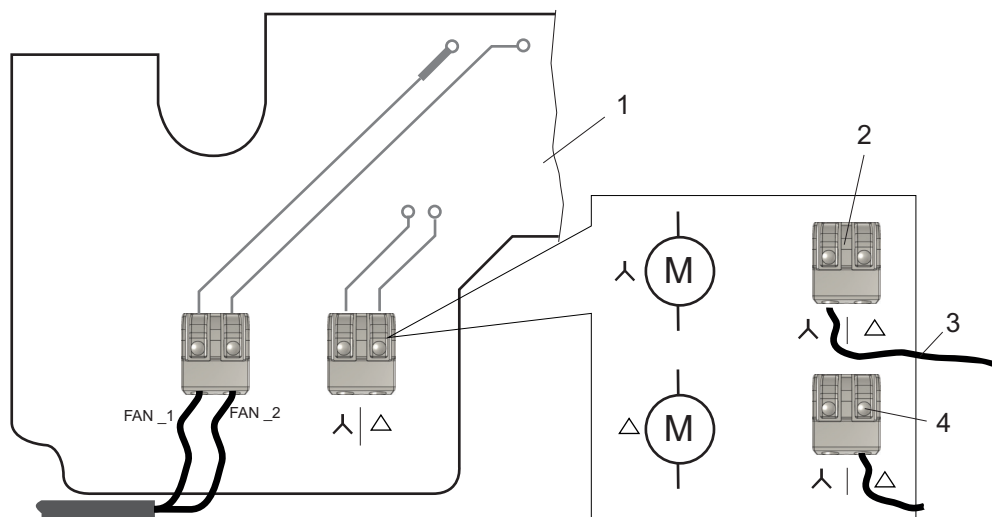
Serrage du câble de raccordement du ventilateur sur la platine
